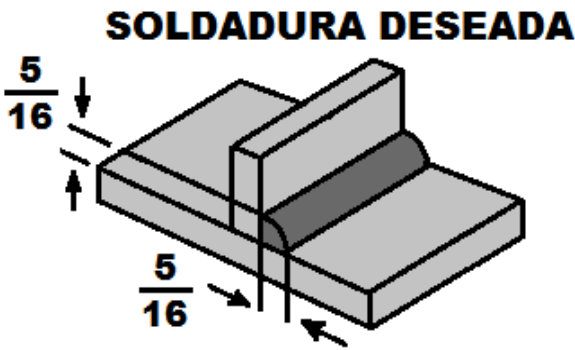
Dimensiones en soldadura en filete (3, 18, 27, 31)
